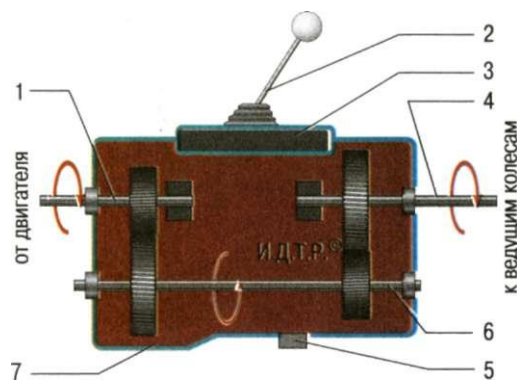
Схема работы коробки передач: 1 - первичный вал; 2 - рычаг переключения передач; 3 - механизм переключения передач; 4 - вторичный вал; 5 - сливная пробка; 6 - промежуточный вал; 7 - картер коробки передач
